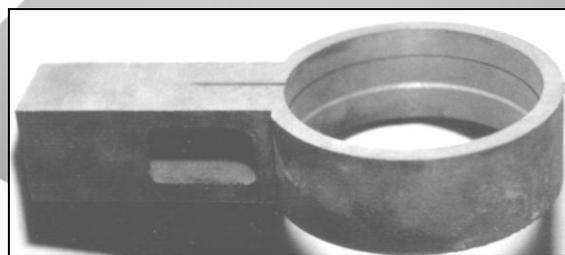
Деталь типу «Плунжер», що оброблюється торцевими фрезами з гексанітом-Р
